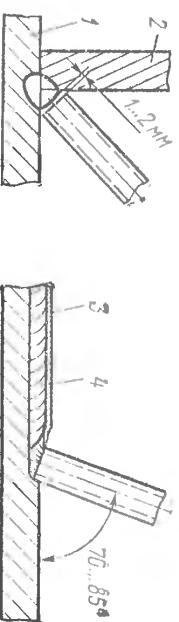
Схема сварки ультракороткой дугой с глубоким проплавлением:
